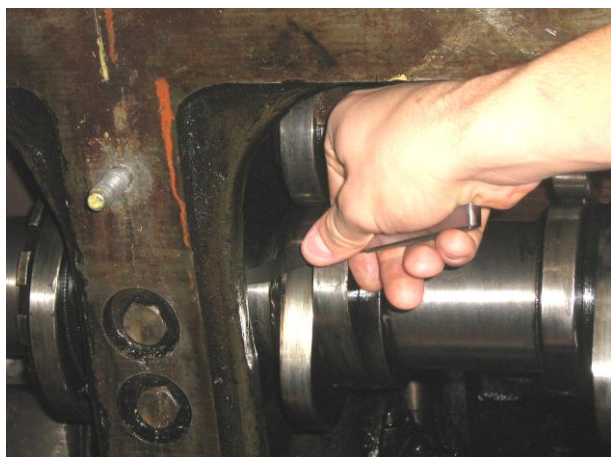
Замер масляного зазора в подшипнике распредвала щупом
